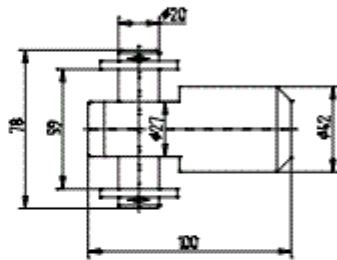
Соединительная тяга для механизмов М30-1600-92К (К6) (в комплекте - вилка и шток)
